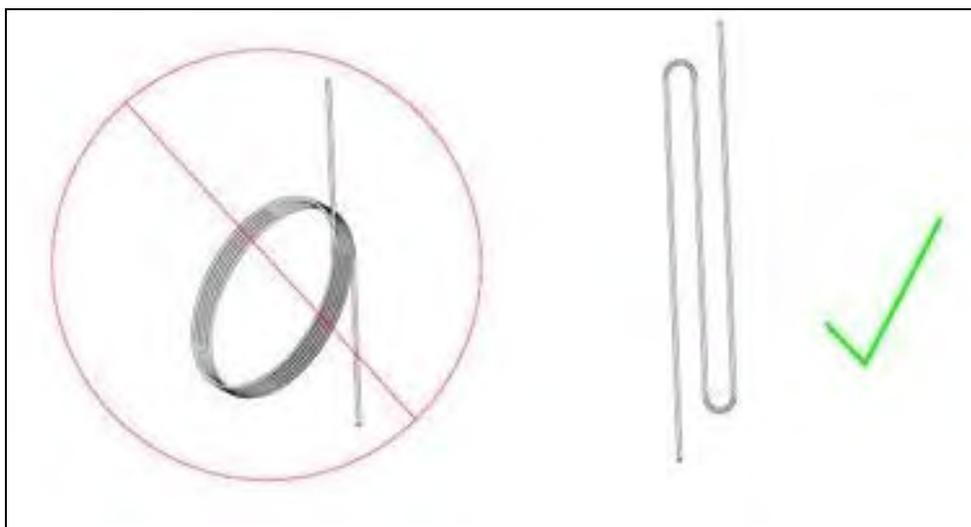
CÂBLES EN SERPENTIN, PAS ENROULÉS
